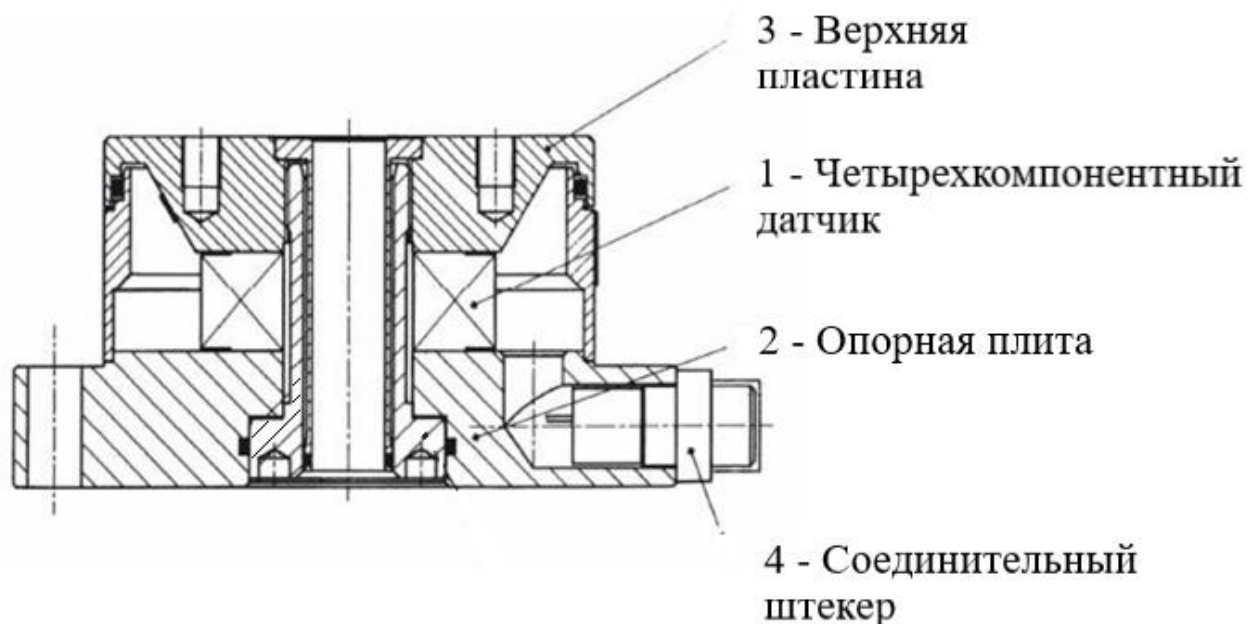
Конструкция пьезодинамометра Kistler 9272 [128]
